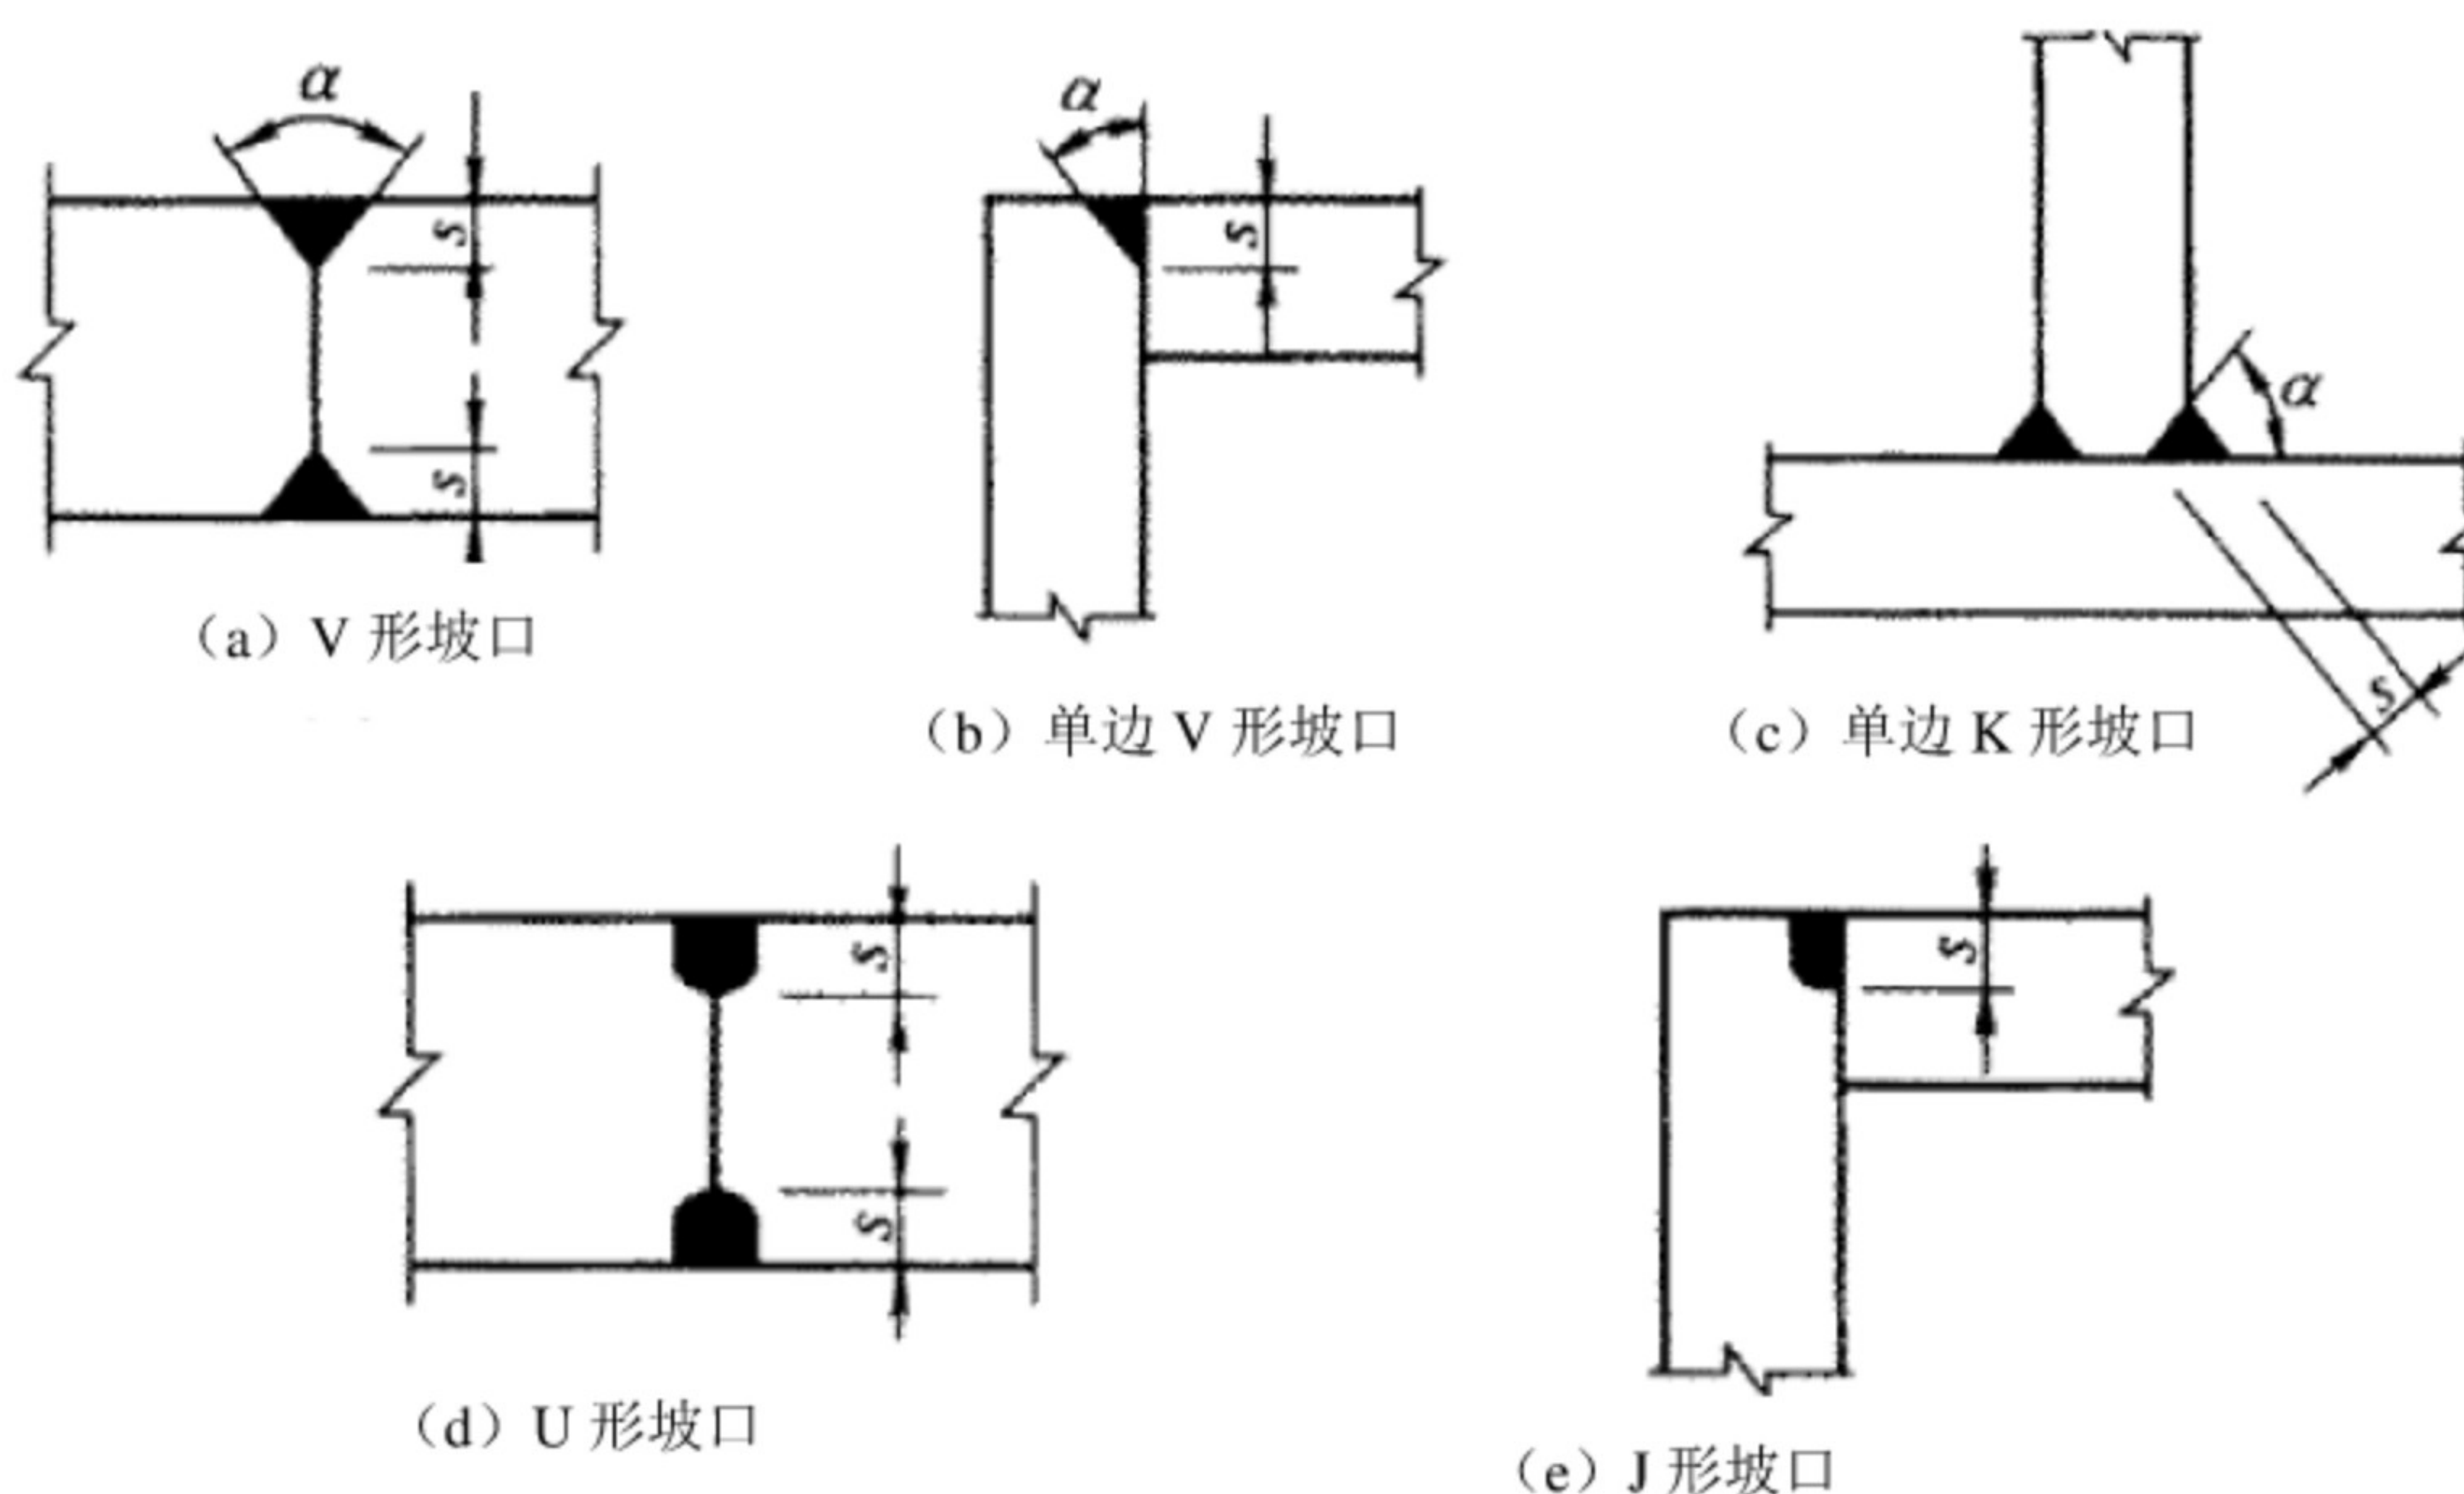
部分熔透的对接焊缝和 T 形对接与角接焊缝的组合焊缝截面
